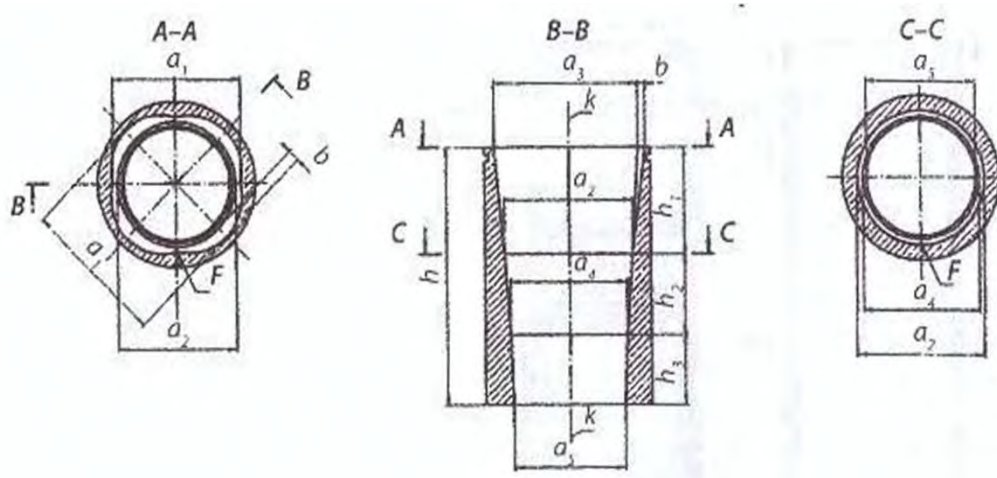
Усовершенствованная конструкция гильзы для литья круглых заготовок
